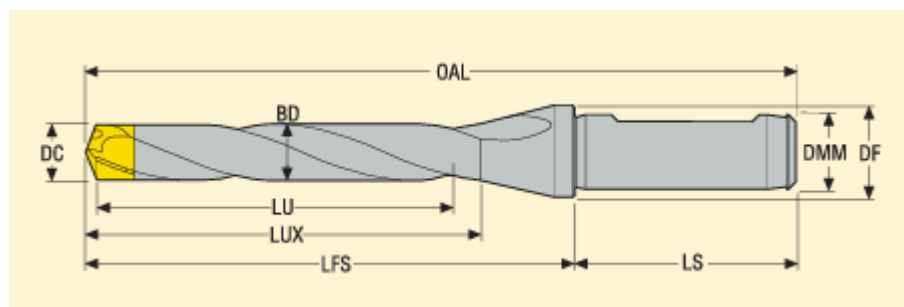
обираємо свердло SD105-22.00/23.99-125-25R7 [2, с 130]
